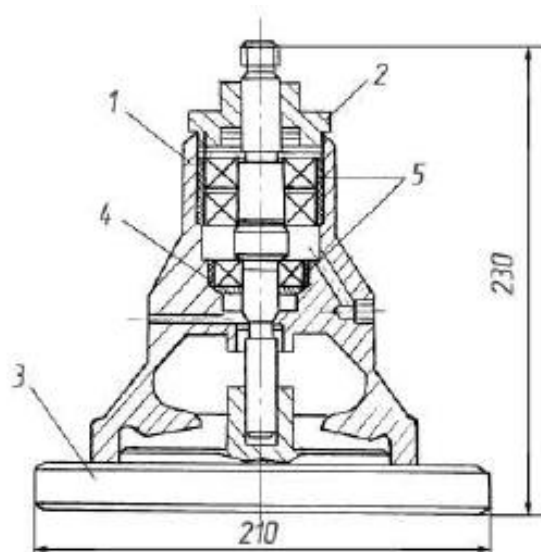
Центруючий пристрій для склеювання корпусу водяного насоса двигуна ЗМЗ-53 з підшипниками на валу: 1 - корпус водяного насоса; 2 - кришка приладу; 3 - корпус приладу; 4, 5 - клей.
